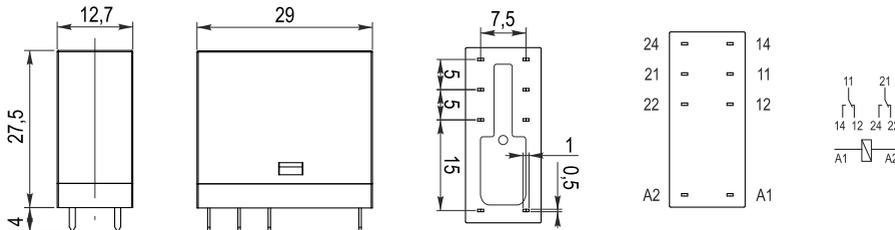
Габаритные размеры, цоколевка и схема подключения реле
